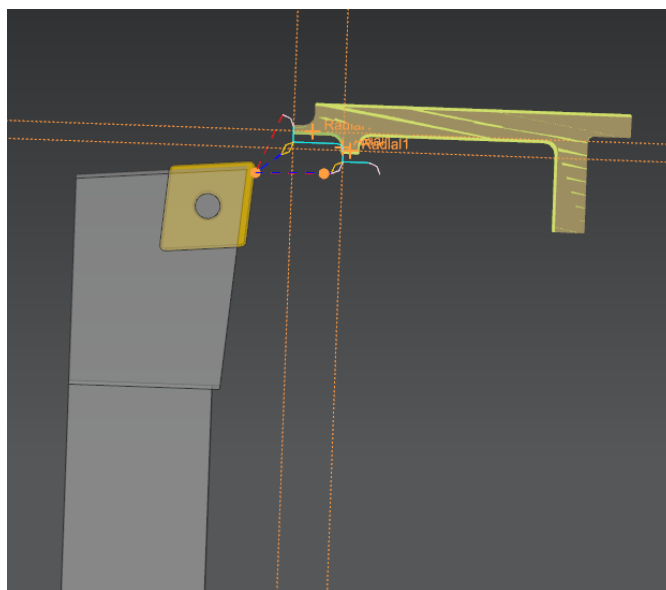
Операции 20 уст.2 пер.1,2,3- Обточка торца, выступа и буртика
